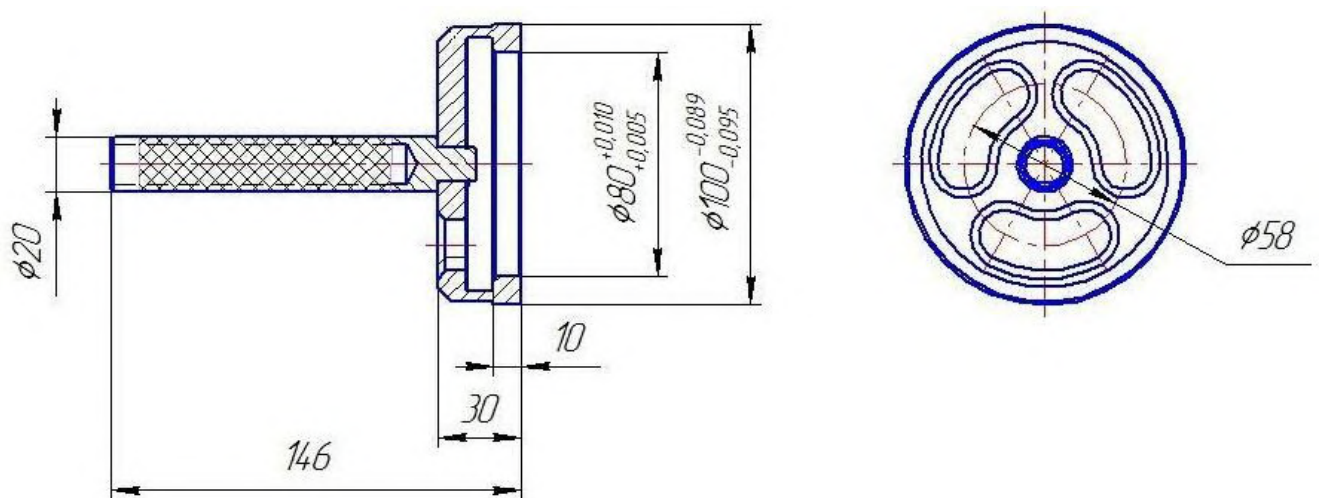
ZM 7853-4418 – Richtvorrichtung zum Zentrieren der hinteren Wellendichtung in Verbindung mit dem Wellendichthalter relativ zum hinteren Flansch der Kurbelwelle
